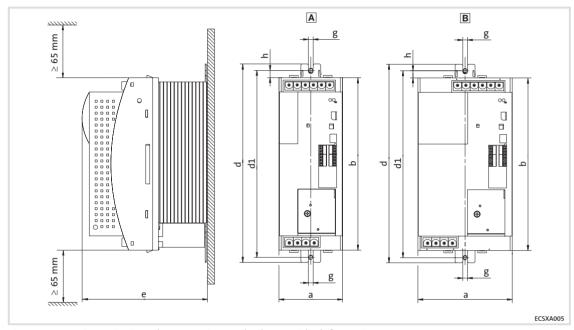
Dimensioni per il montaggio standard con guide di fissaggio
